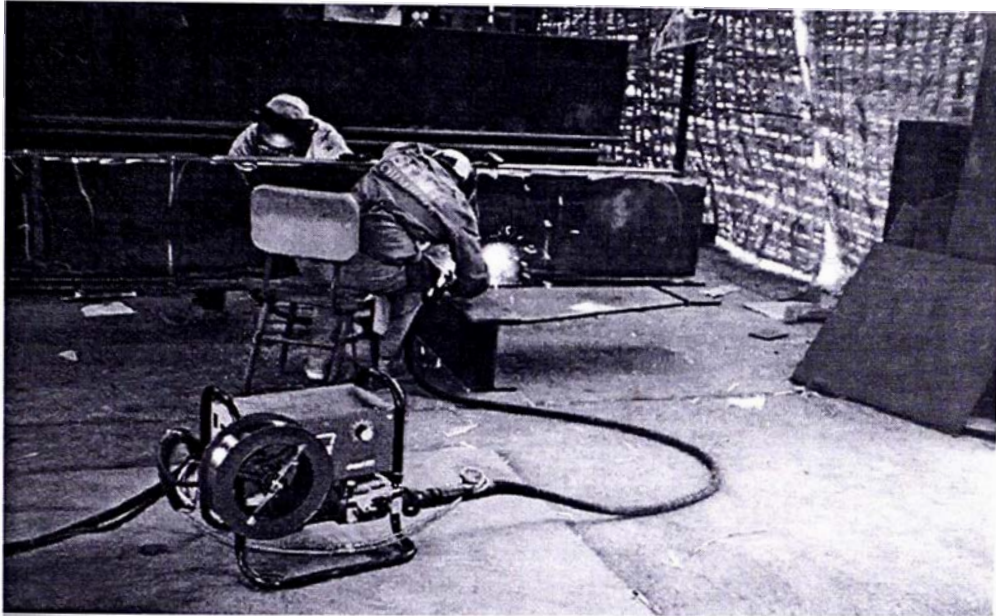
Soldadura de un Miembro de la Brida Superior, mediante proceso MIG/MAG
